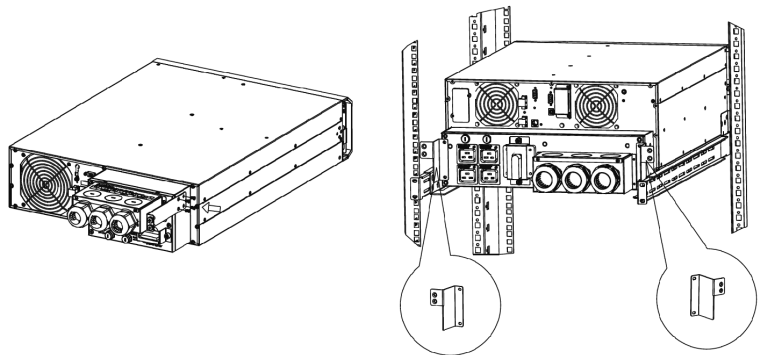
Соединительный блок с уголком (-ами) крепления для окончательной сборки сзади Protect D.
